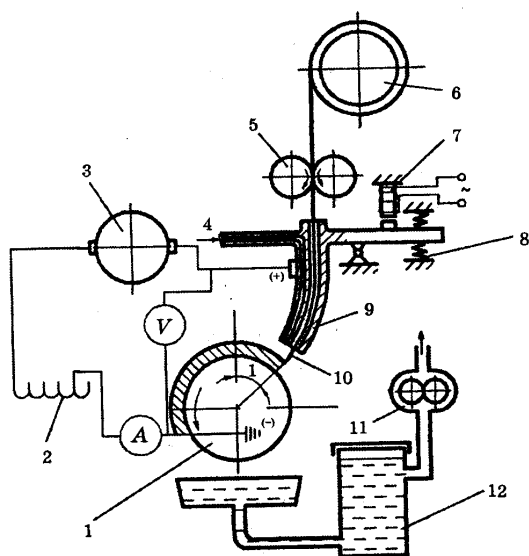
Схема установки для вібродугового наплавлення деталей
